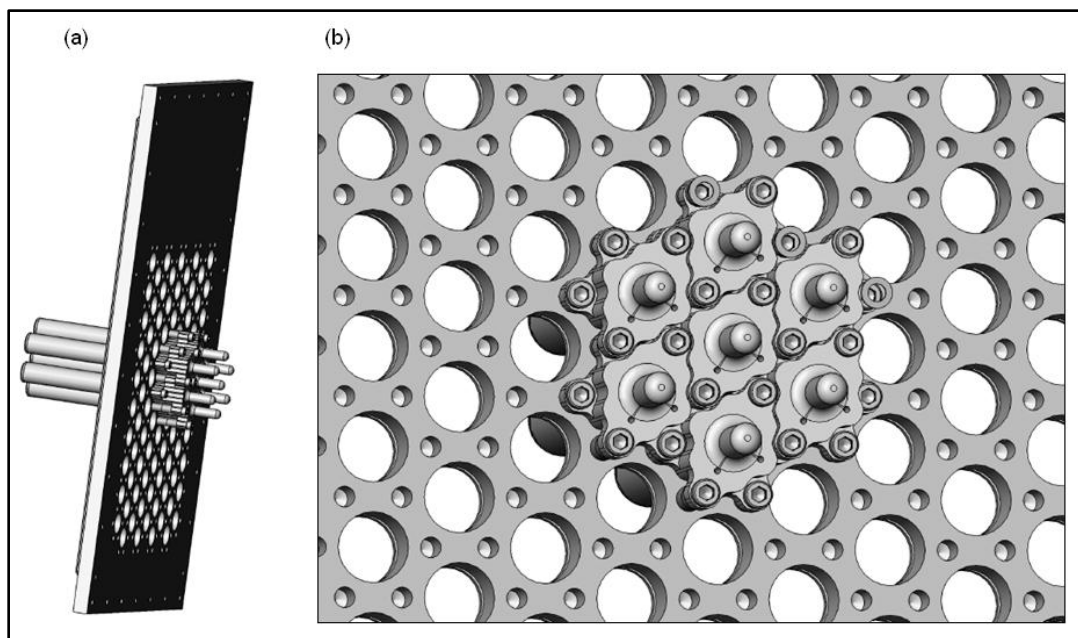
Exemple de fixations des tubes en grappe sur la paroi (a) : Vue de côté de la plaque entière (b) : vue de dessus sur les dispositifs de fixation
